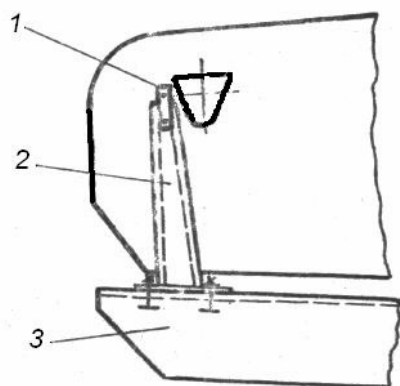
Схема привода подвижной перегородки: 1 — рычаг; 2 — колебатель; 3 — боковина решетного стана.
